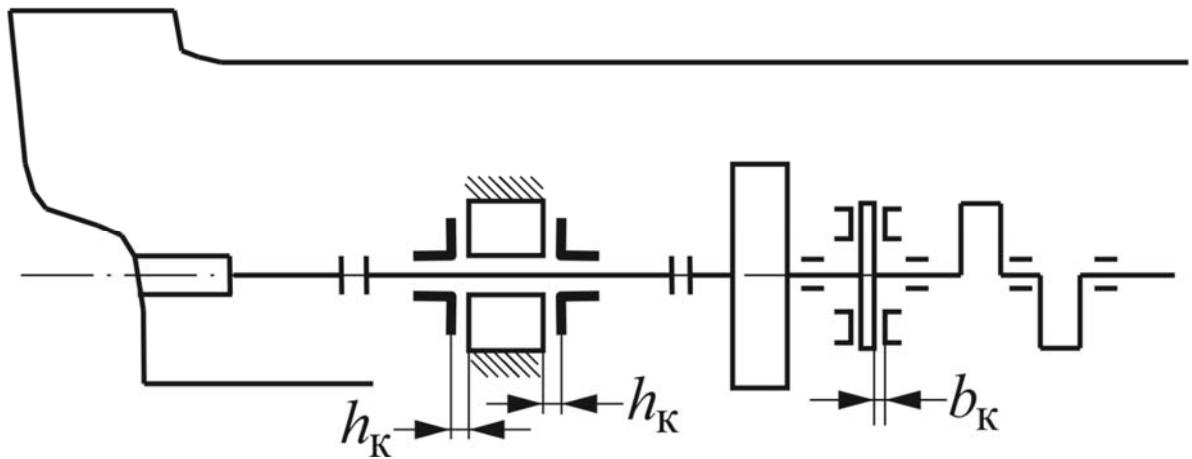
Схема перевірки зазорів в упорних підшипниках.
